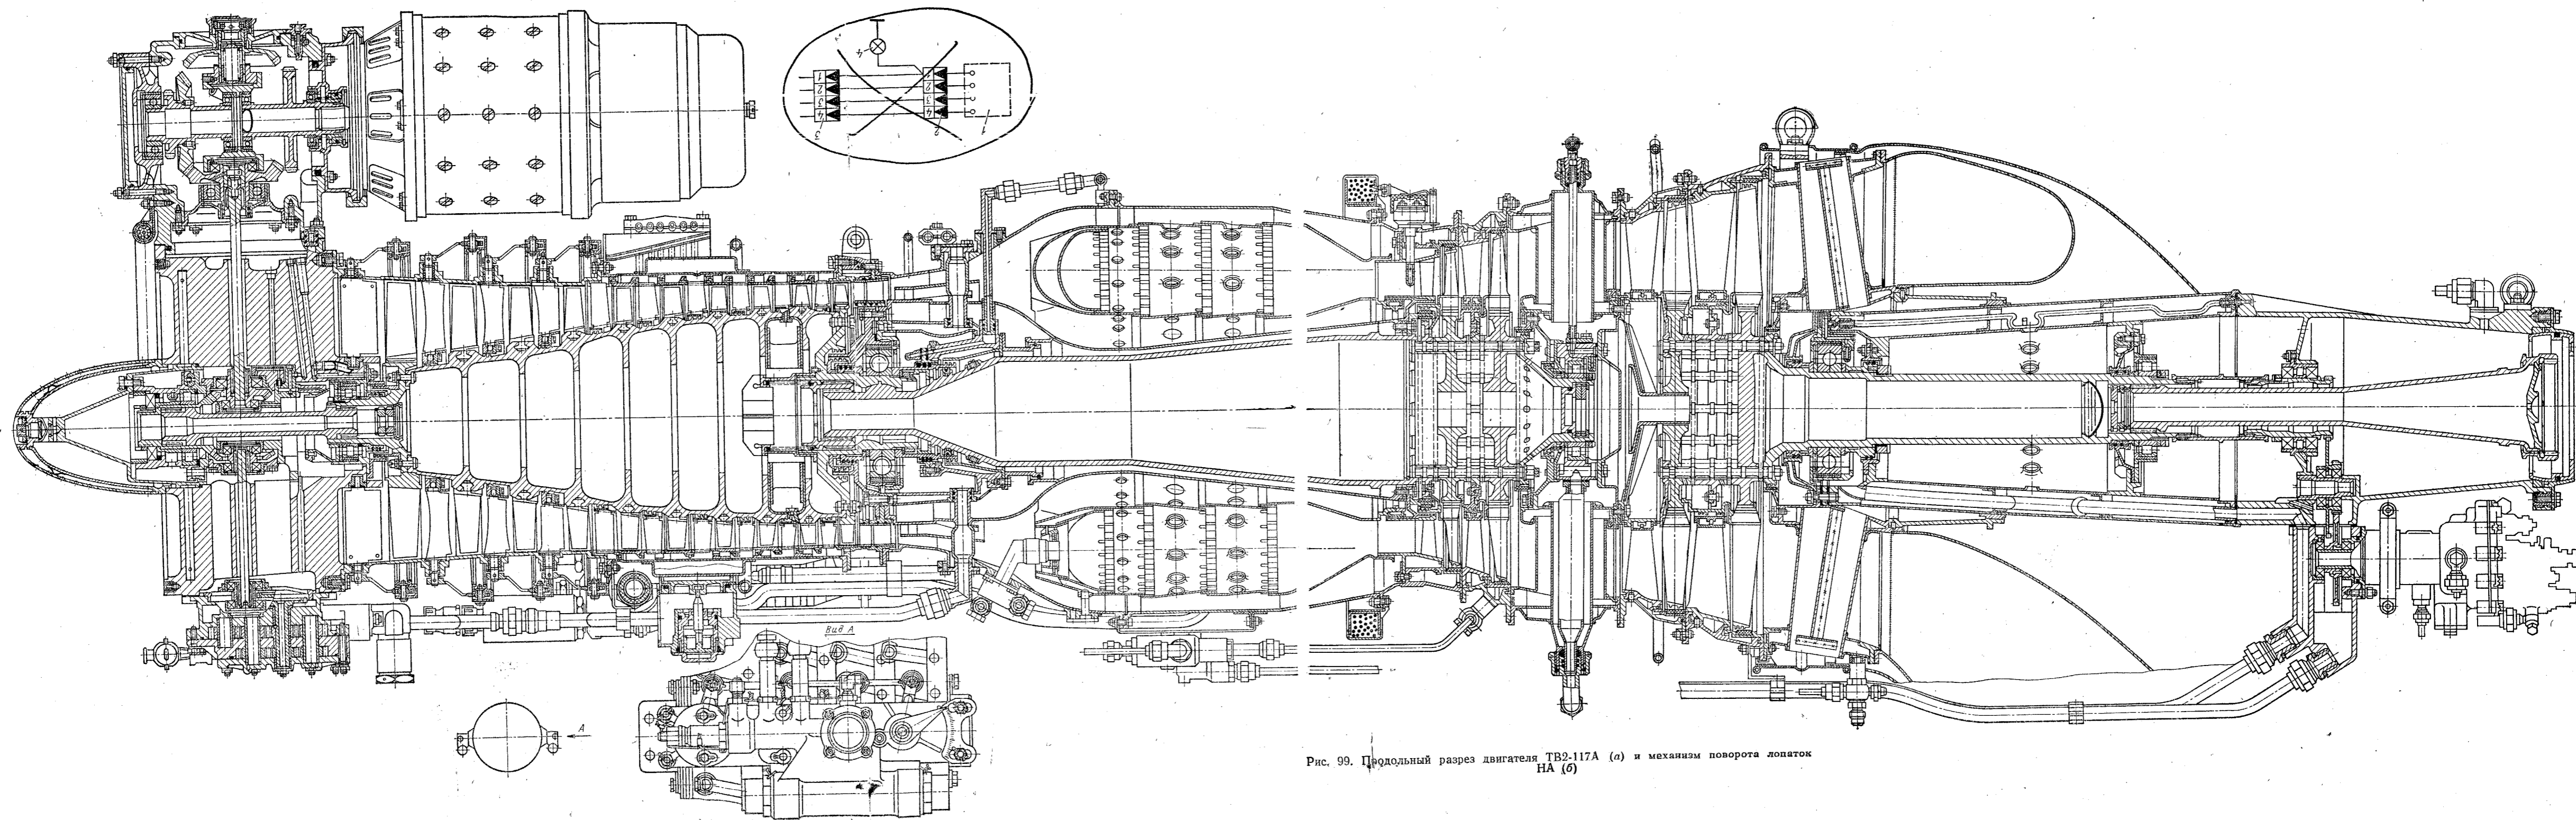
Продольный разрез двигателя ТВ2-117А (а) и механизм поворота лопаток
